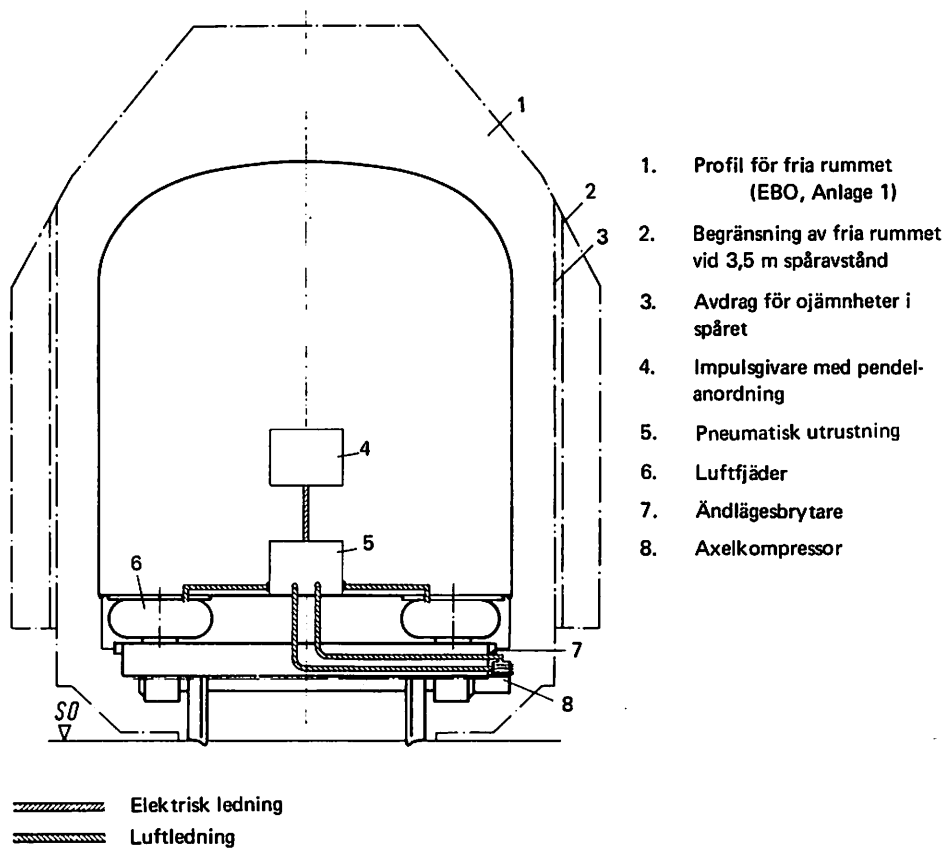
16 Principskiss över system för vagnslutning i det tyska dieseldrivna motorvagnståget VT 624.
